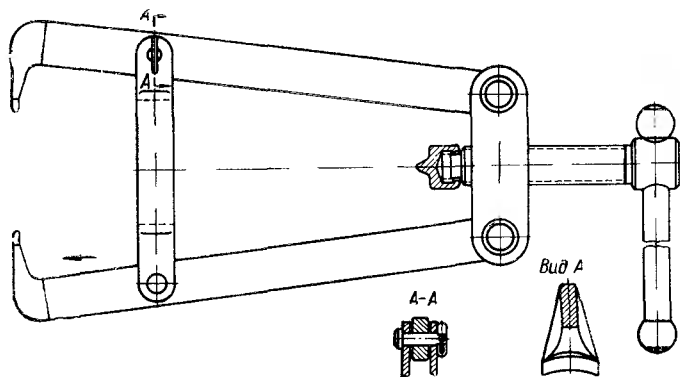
Съемник внутренних колец подшипников вала ведущей конической шестерни
